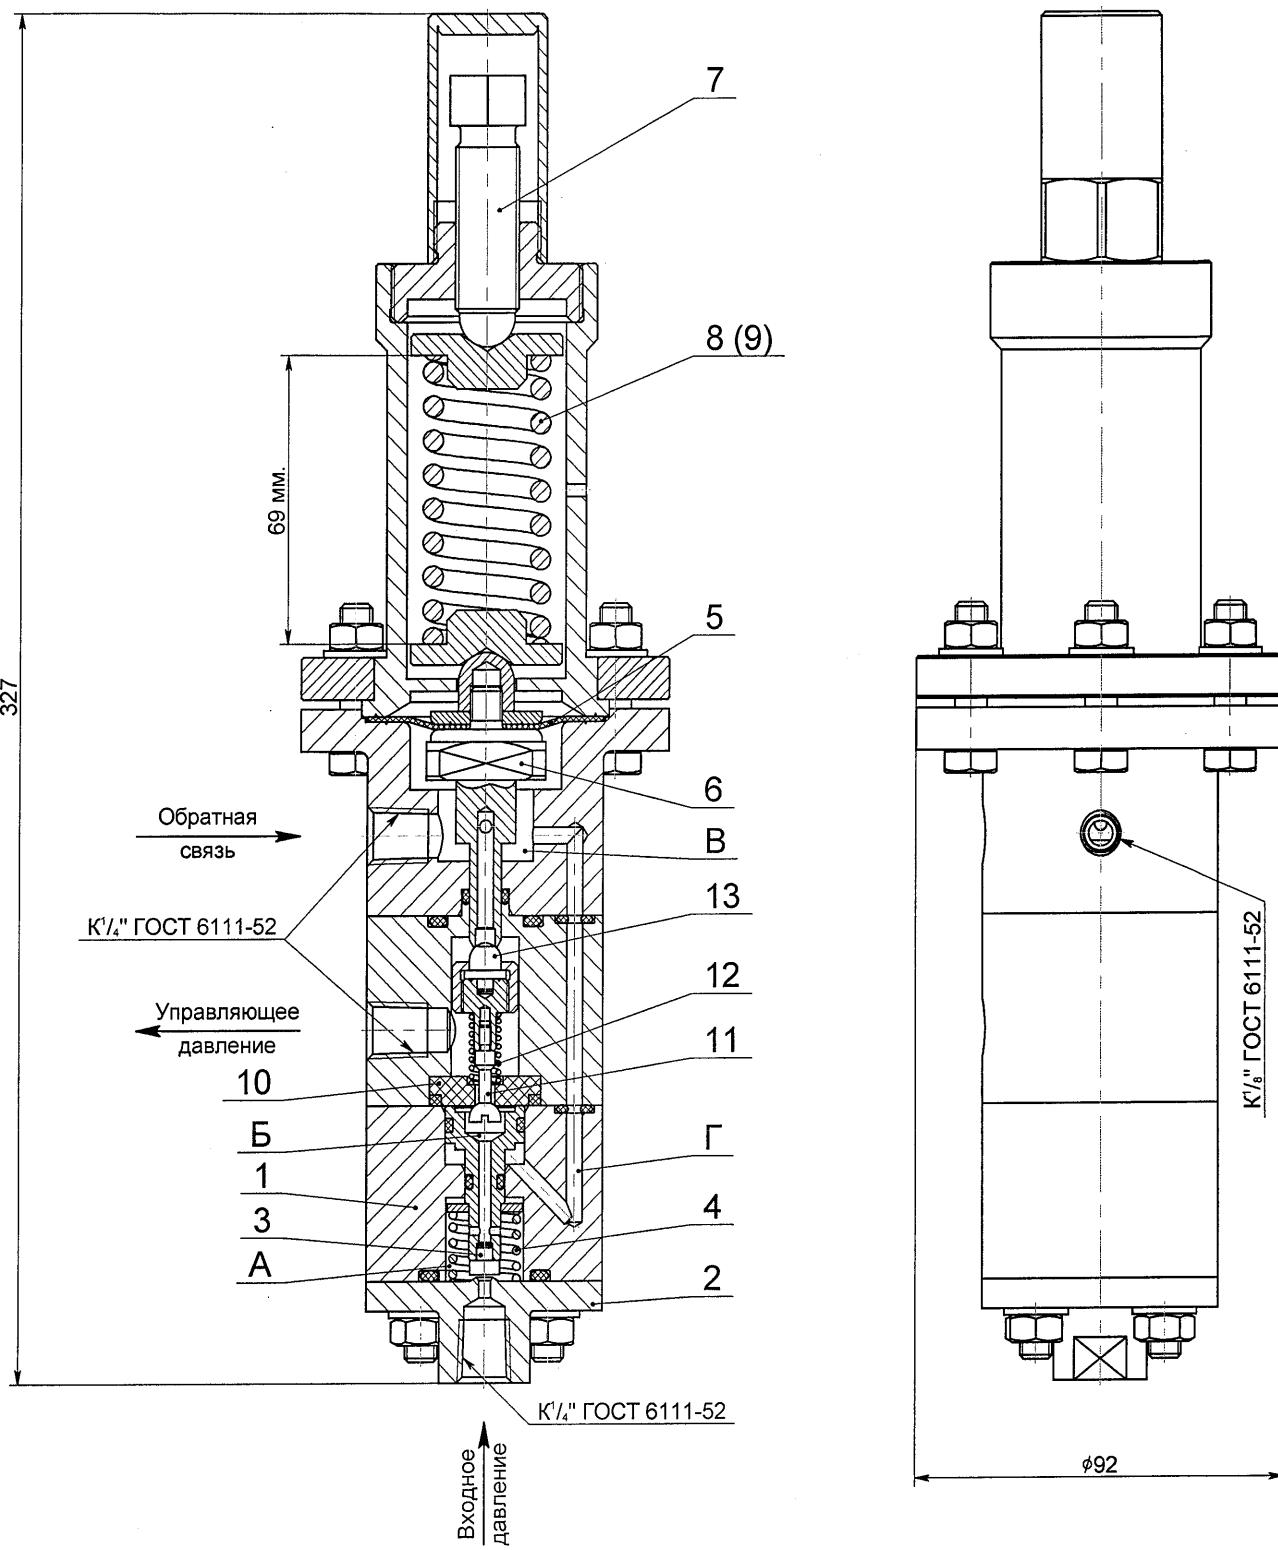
Общий вид, габаритные и присоединительные размеры устройства задающего.
